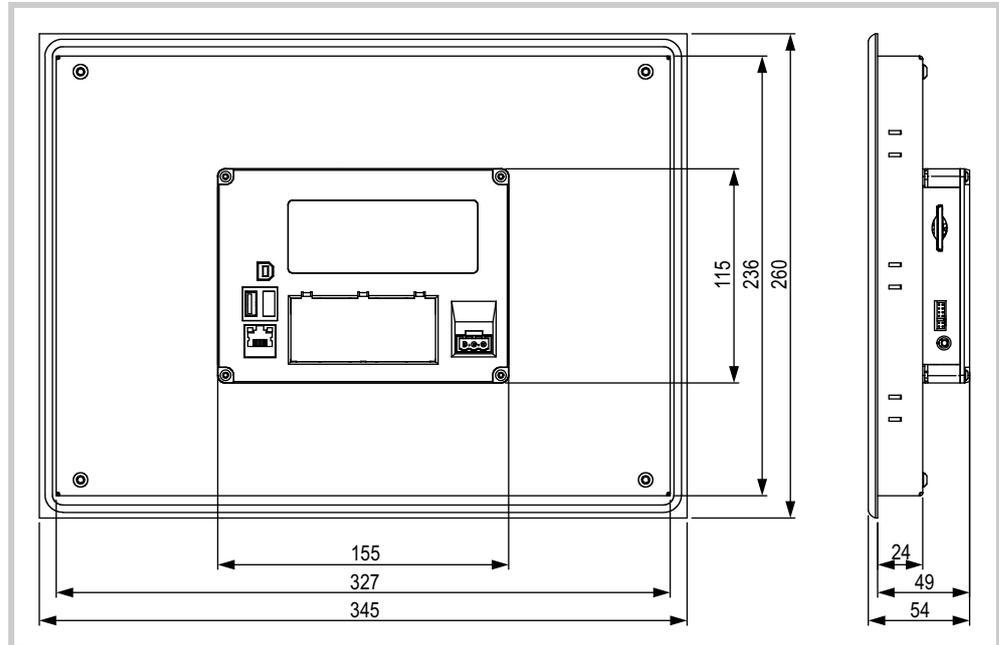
Mechanische Abmessungen der 10,4"-Geräte in mm
